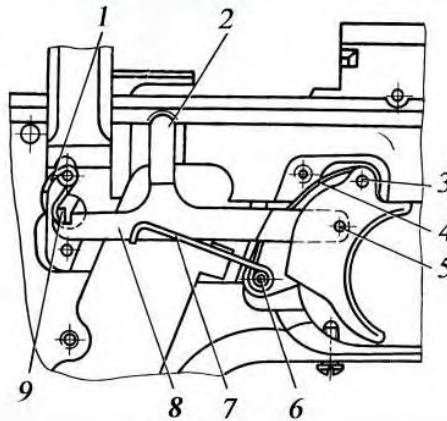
Пусковой механизм: 1 – пружина шептала; 2 – разобщик;
